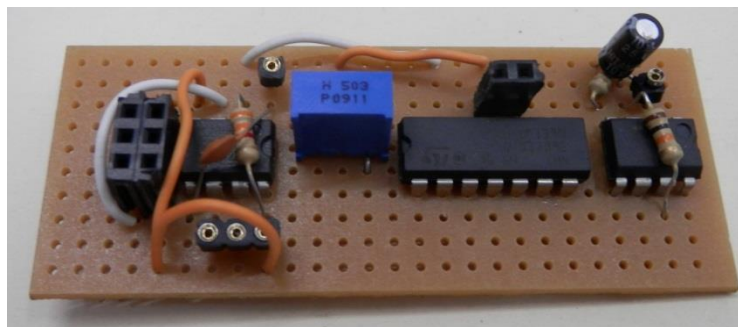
Receptor de pulso ultrasónico , versão soldada
